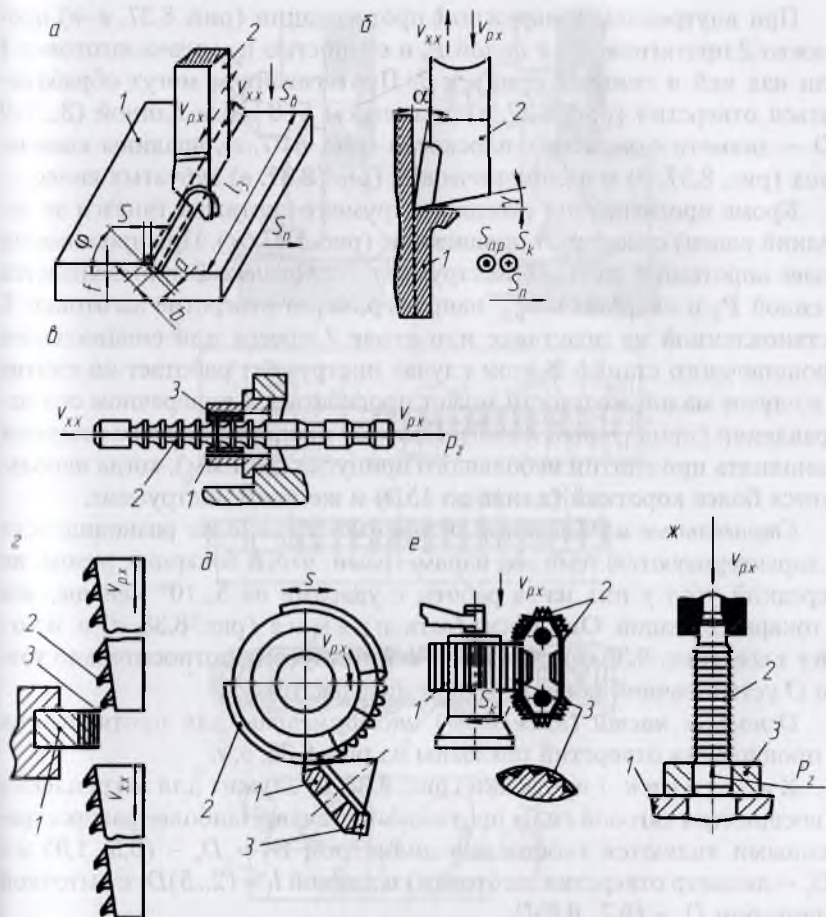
Схемы обработки: строганием (а), долблением (б) плоских поверхностей, протягиванием внутренней (в), наружной плоской (г) поверхностей, шпиди зубчатых конического (д) и цилиндрического (е) колес, прошиванием отверстия (ж)
